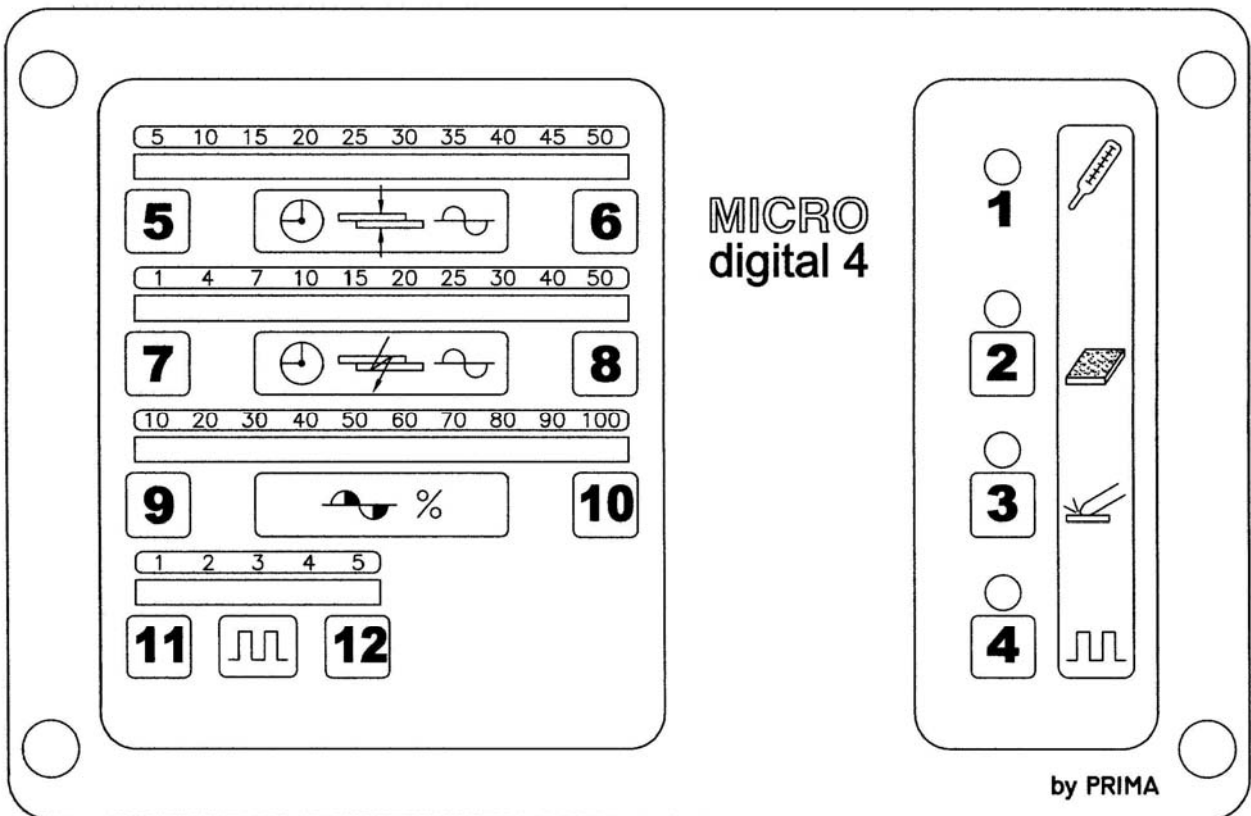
Frontal del control de soldadura tipo MICRO DIGITAL 4
